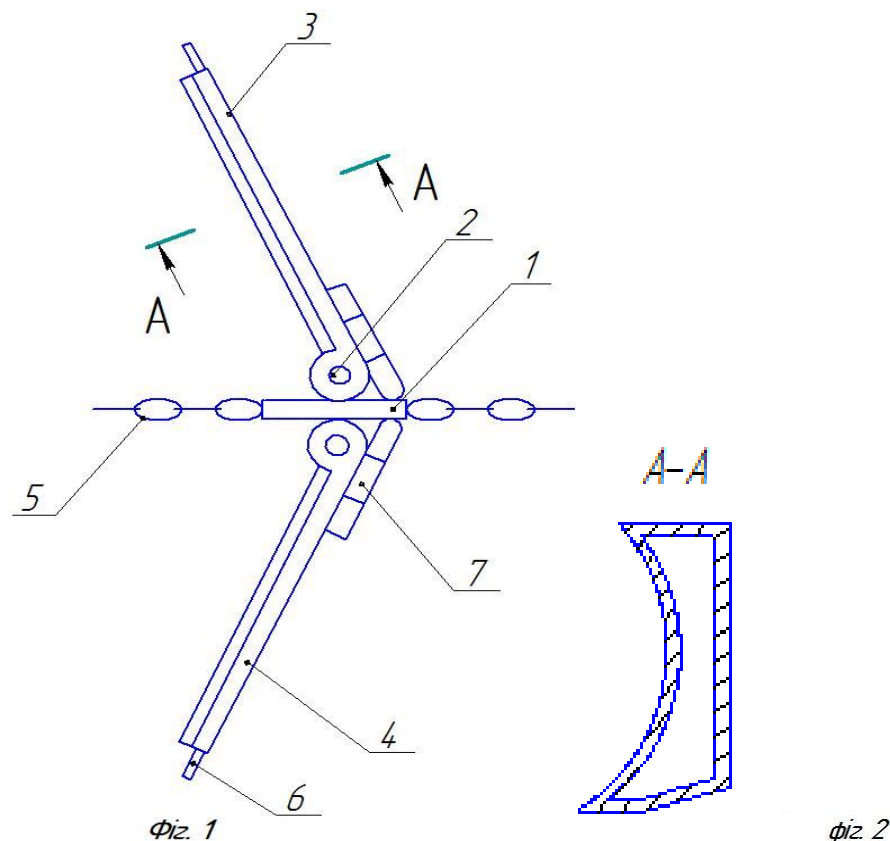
Розроблений скреперний пристрій для прибирання гною.
